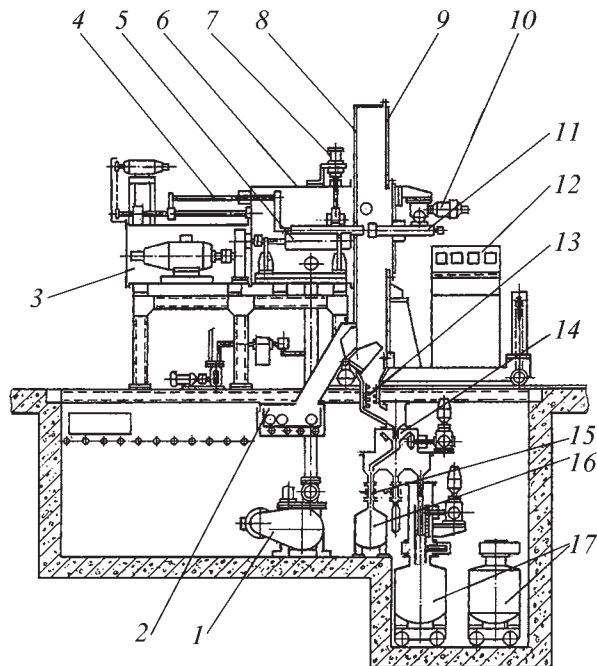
Установка типа УЦР плазменной плавки и центробежного распыления быстровращающейся литой шлифованной заготовки:
